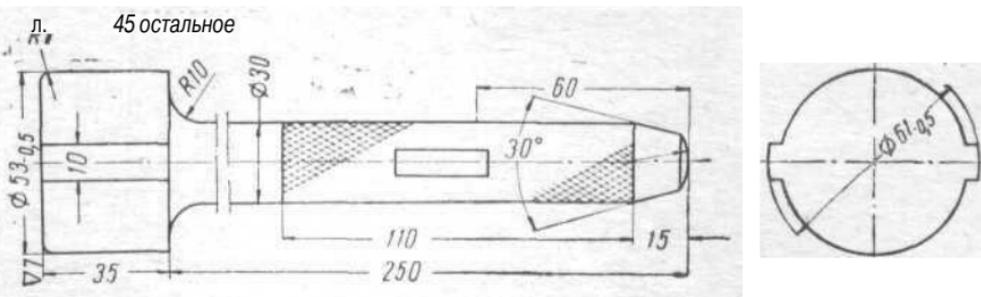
Оправка для выпрессовывания переднего подшипника вала ведущей шестерни главной передачи одновременно с сальником
